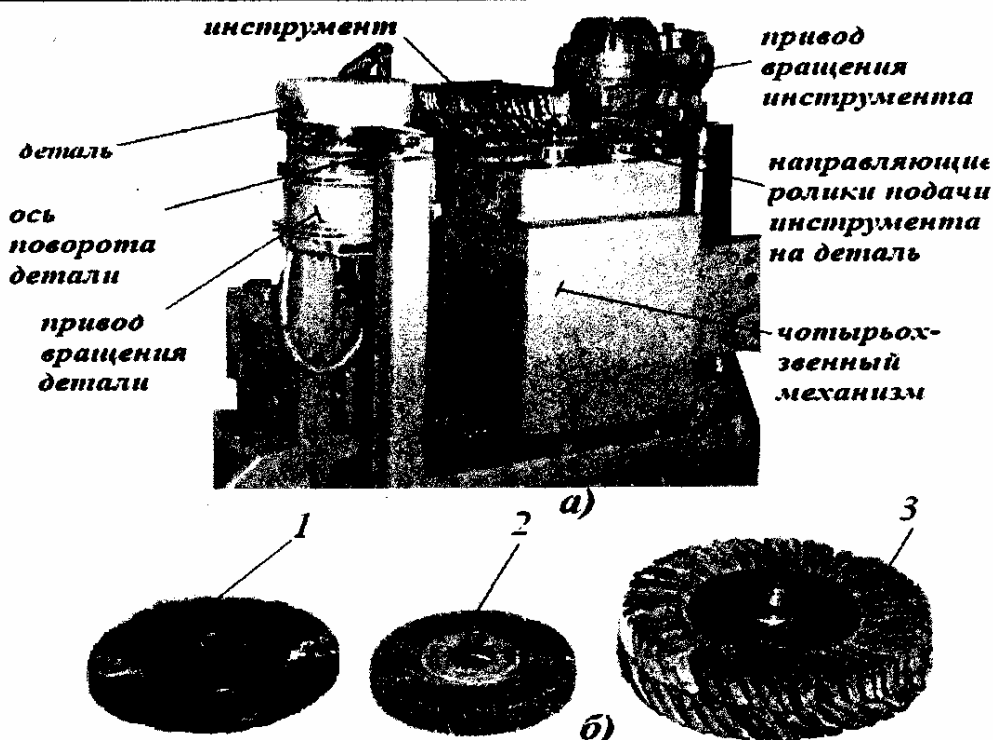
Оборудование для обработки светорассеивающих поверхностей тонкостенных деталей (а), абразивный и лезвийный инструмент (б):
